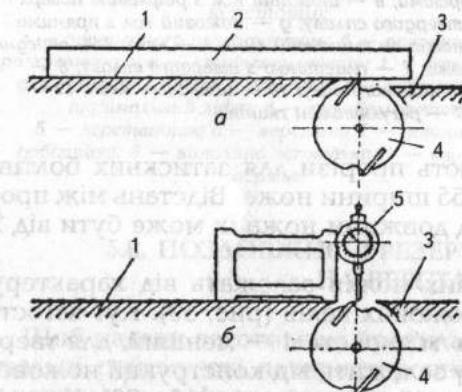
Перевірка положення різальної кромки ножа фугувального верстата щодо робочої поверхні заднього стола:
